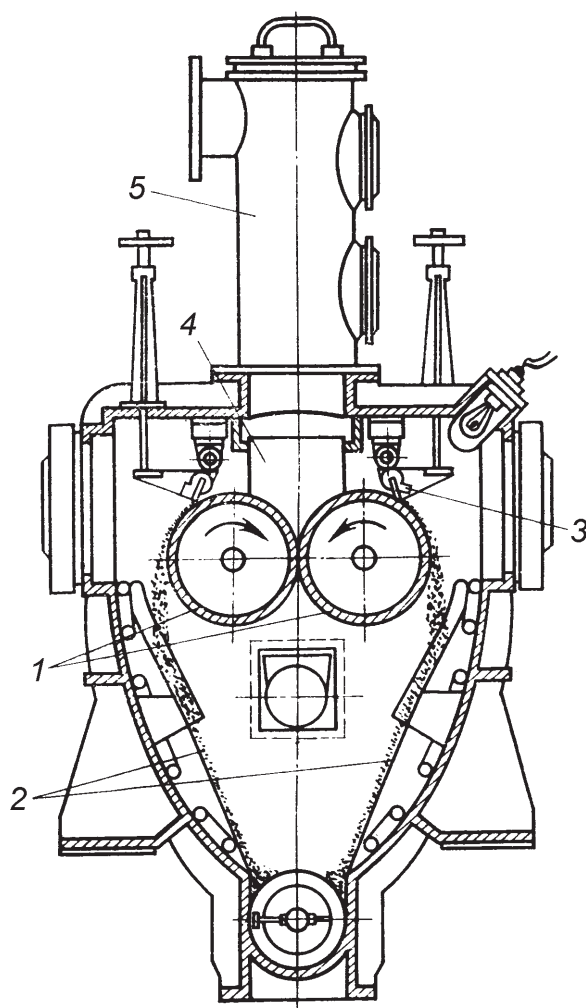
Схема вакуумной двухвальцовой сушилки:
